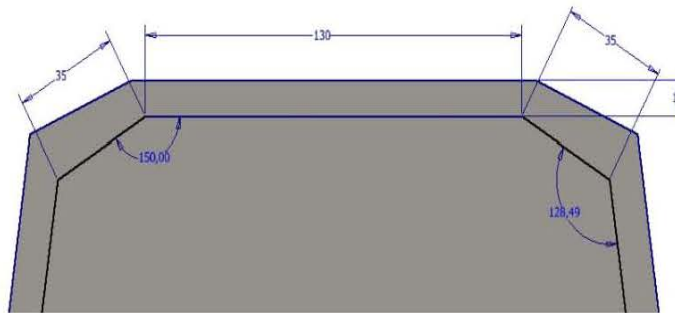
Hasil *Dimension* Sandaran Kursi 2
